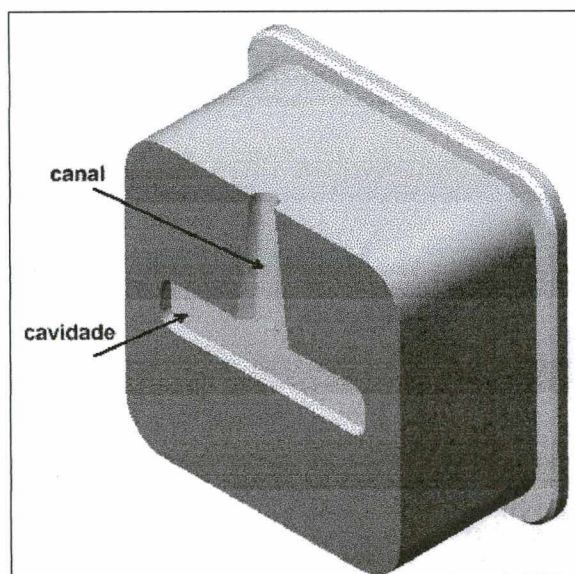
Insertos do experimento com moldagem de pós-metálicos (imagens do CAD)
